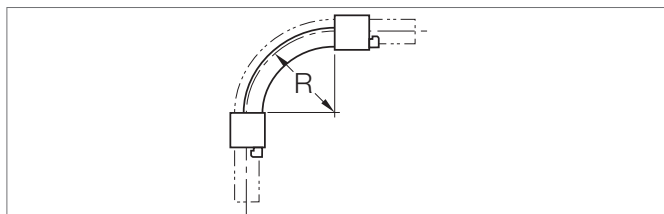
Bockfixtur sanitet 90 grader för dimension 16–32 och bockfixtur sanitet/värme 5 x d 90 grader för dimension 32
